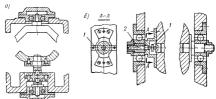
Схема крепления подшипников с гладкой внутренней поверхностью наружного кольца
